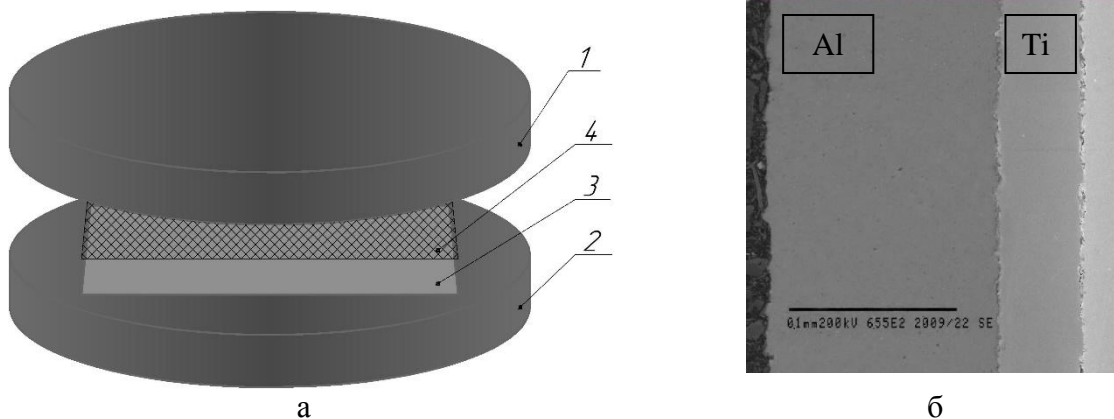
Схематичне зображення оснащення для зварювання фольги по схемі вільного деформування через сітку (а) і мікроструктура біметалевих з'єднань АІ+Ті: 1, 2 – верхній та нижній фланці; 3 – пакет з фольги, що підлягає зварюванню; 4 – сталеві сітка
